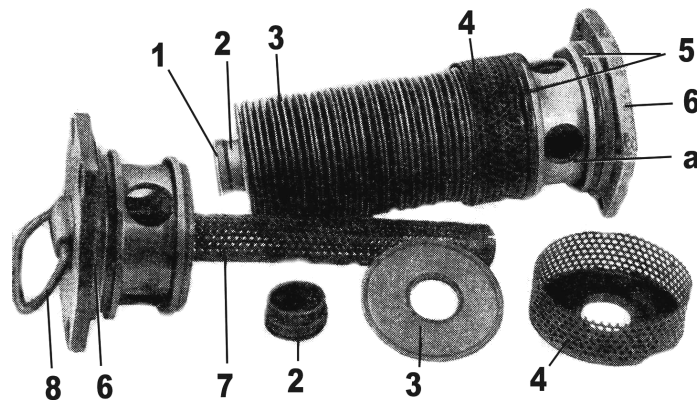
Фильтрующий элемент: 1 – стопорное кольцо; 2 – гайка; 3 – фильтрующие элементы; 4 – защитная сетка; 5 – резиновые кольца; 6 – крышка; 7 – стержень; 8 – ручка; *а* – окно
